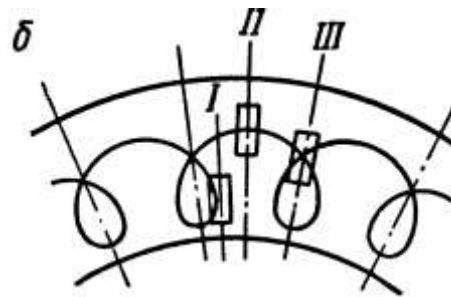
Притирання коротких циліндричних деталей на верстаті з двома дисками:
